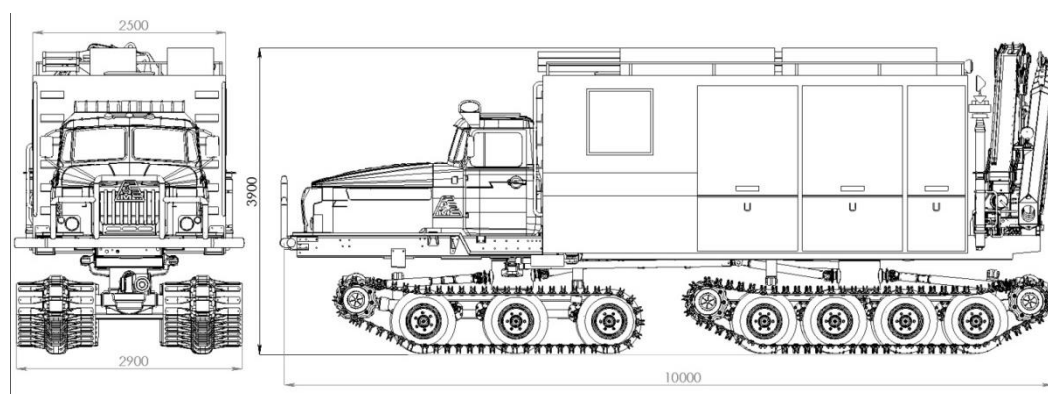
Опытный образец ТТМ (пожарно-спасательная машина АСМ-20-06)
